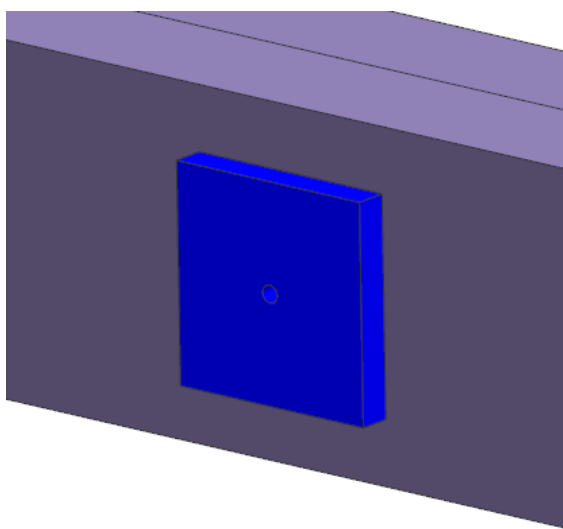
Типовой вид площадки под мишень лазерного трекера.
